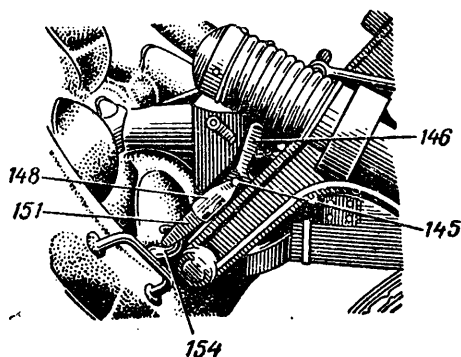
Приспособление старой конструкции для крепления по-походному опорной плиты. Плита закреплена в походном положении:
